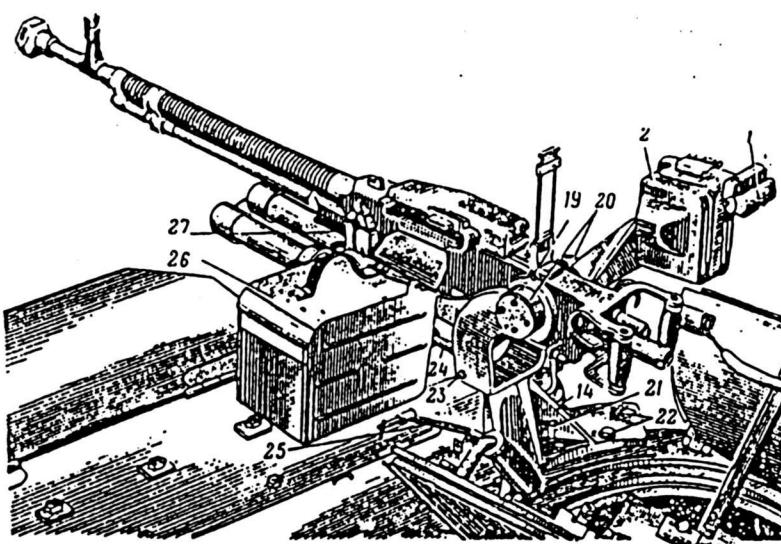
Зенитная установка 12,7-мм пулемета ДШК (вид слева):
